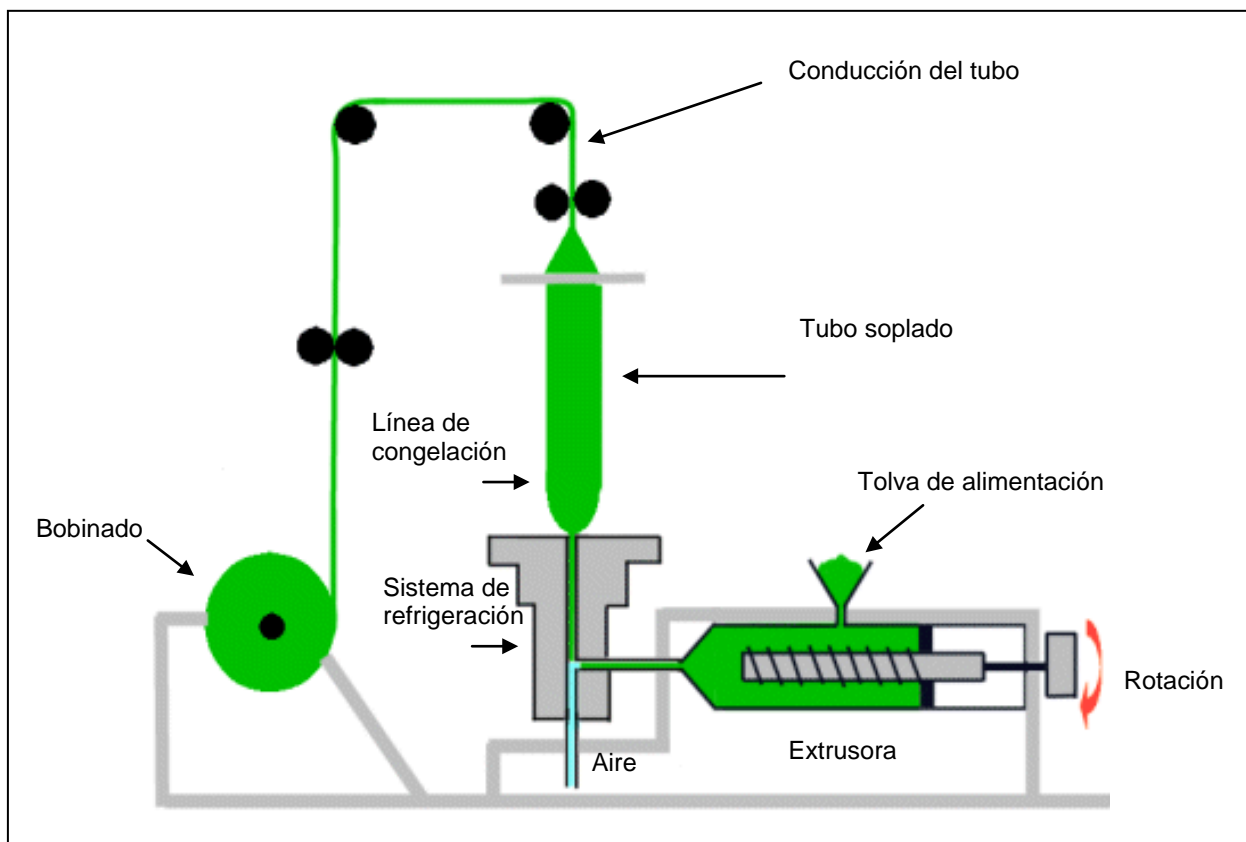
Proceso de extrusión. Fuente: Matières Plastiques Techniques
